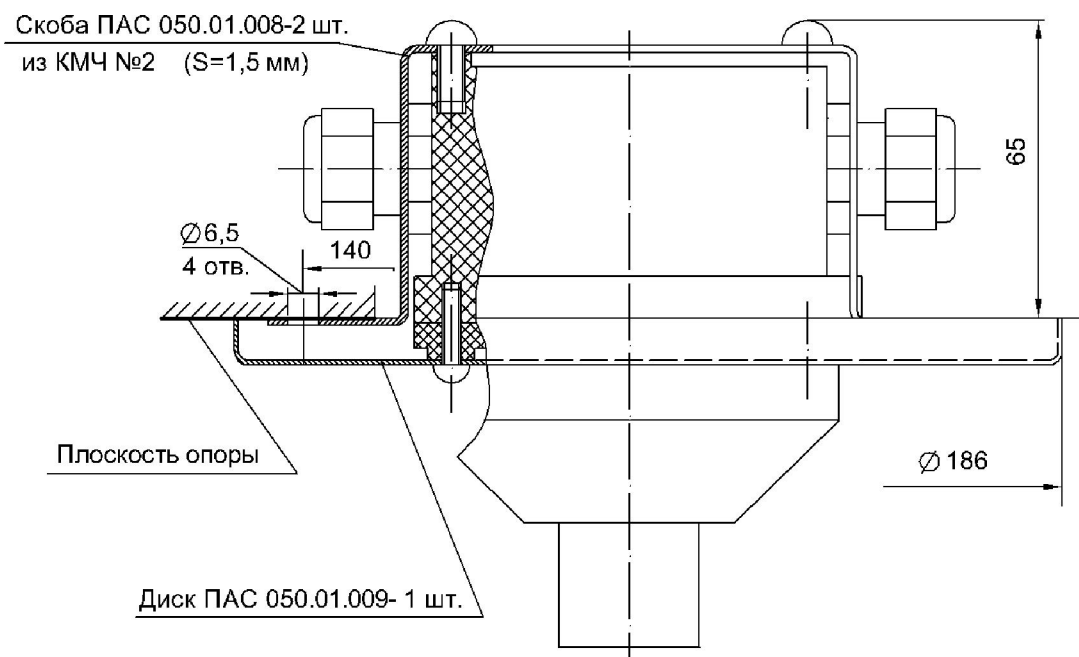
Крепление извещателя ИП212/101 – "Барк М-И" скобами
